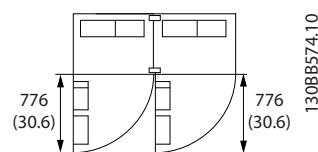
Пространство перед корпусом типа IP21/IP54, типоразмер F10
